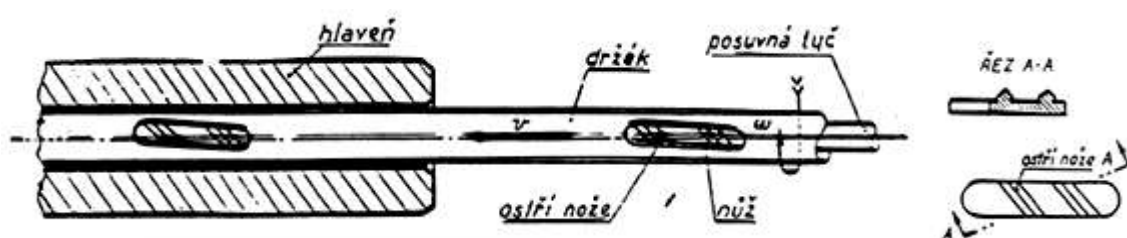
Jednobřítý drážkovací nástroj [12]
